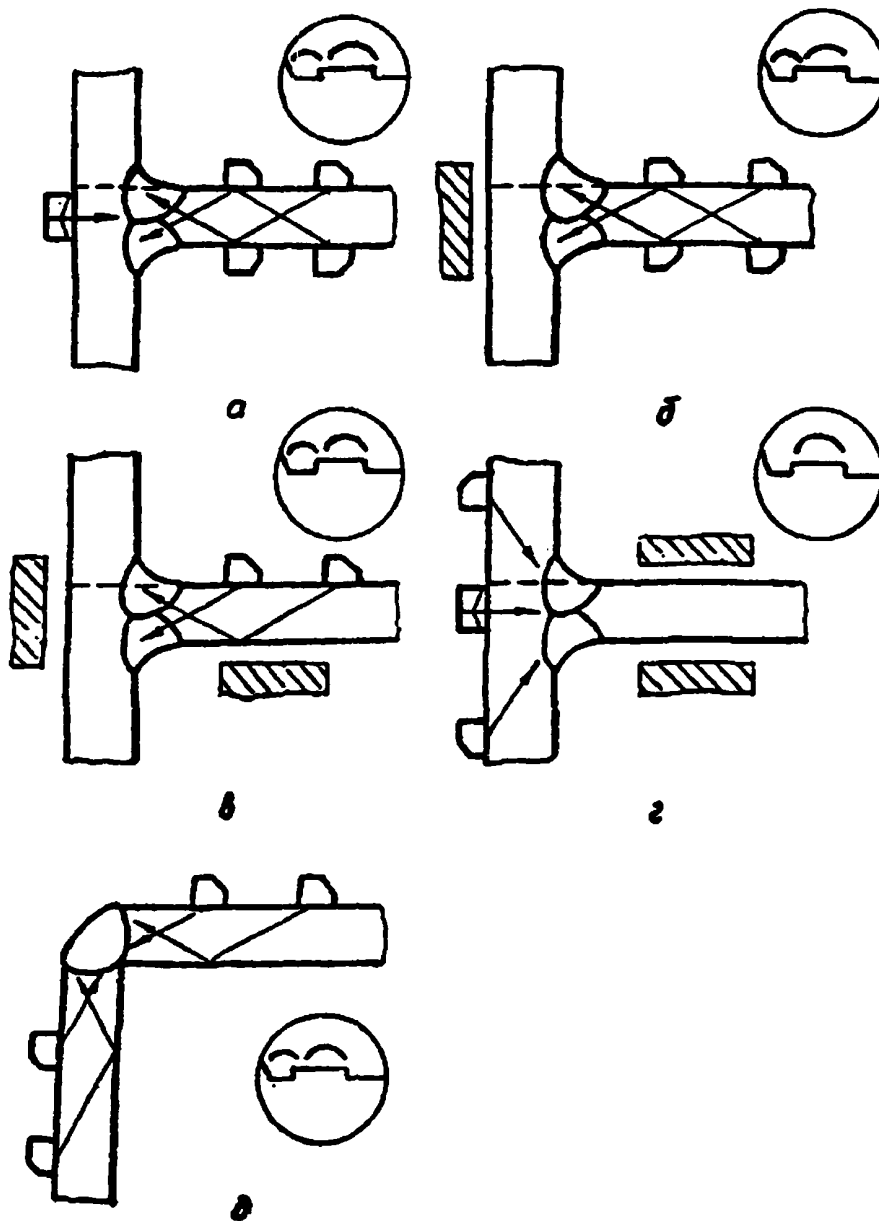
Схемы контроля угловых и тавровых сварных соединений без конструктивных непроваров;
